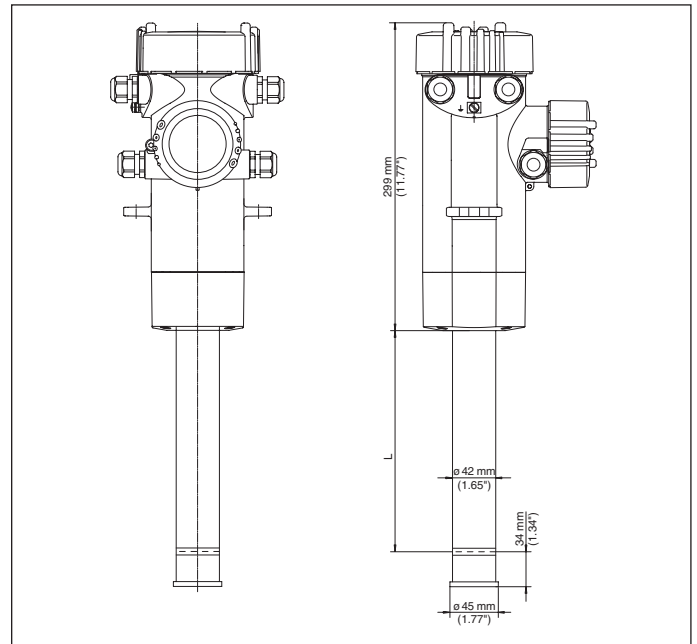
Корпус из алюминия или нержавеющей стали (точное литье)
